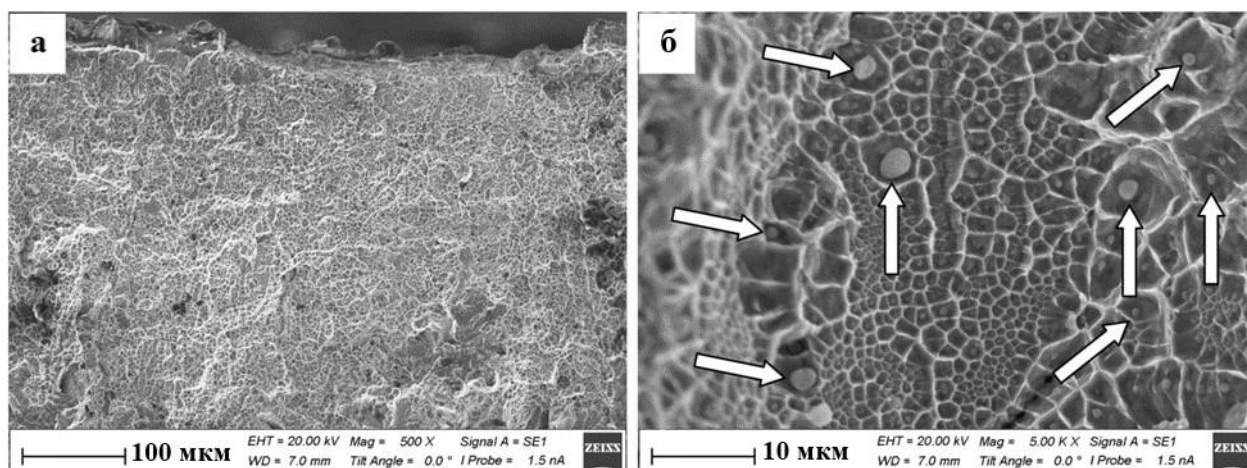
Ямки отрыва вязкого излома наплавленного металла (стрелками на (б) указаны частицы второй фазы)
